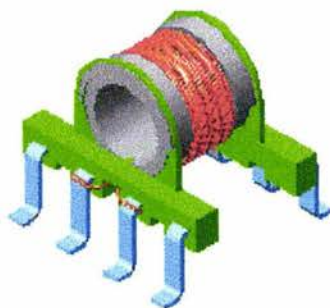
Bobina con el primer embobinado (pieza B). (Cortesía de Midcom Inc.).
